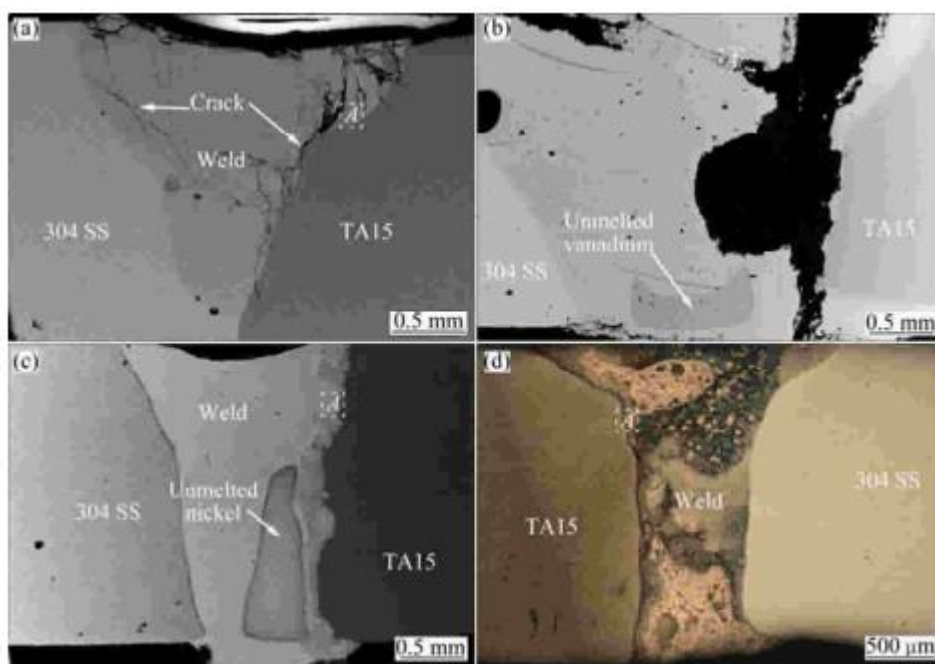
Микроструктуры поперечных сечений соединений с различными присадочными металлами: а – без присадочного металла; б – ванадий; с – никель; d – медь
